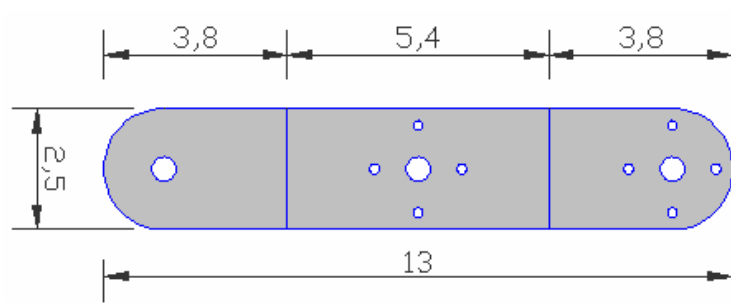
Dimensión tipo U, para giro de patas del robot hexápodo.
